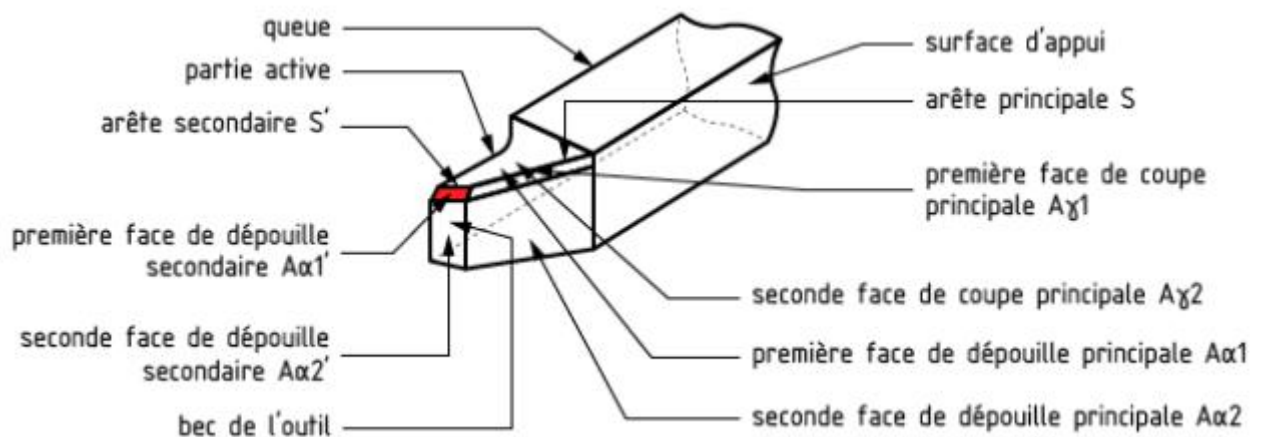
Les principales arêtes et surfaces d'un outil de tournage
